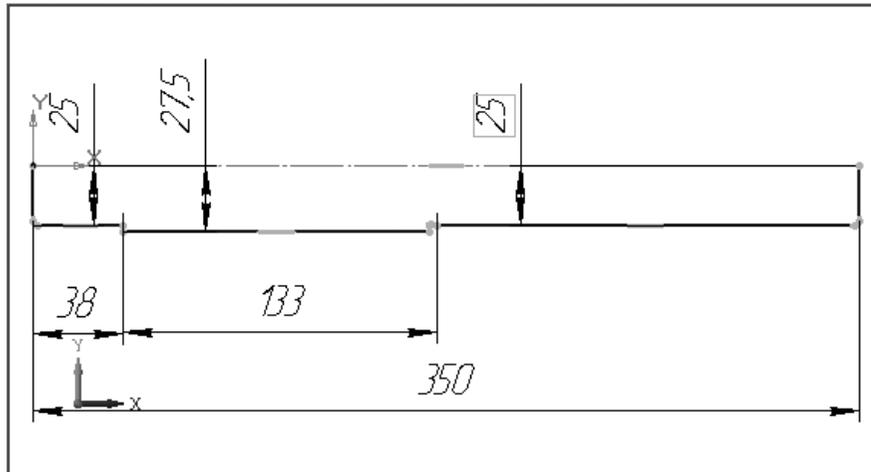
Эскиза вала в режиме построения эскиза с проставленными размерами
